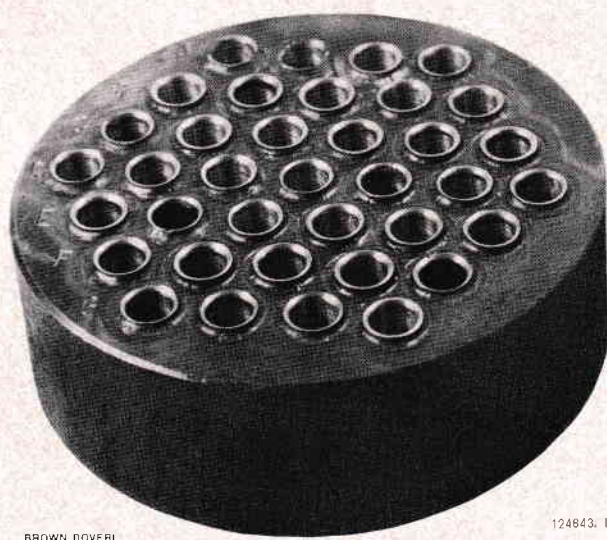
Objet d'essai avec cordons de soudure
